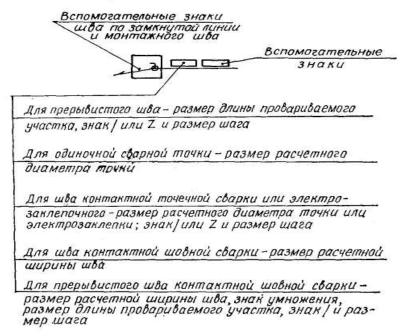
Схема структуры обозначения нестандартного шва или одиночной сварной точки
